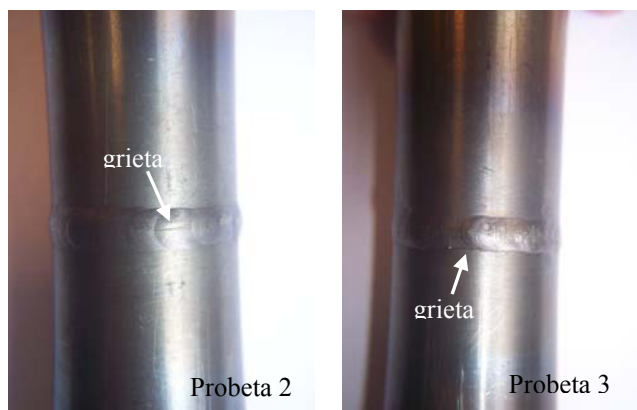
Aspecto de las probetas 2 y 3 tras el ensayo. Se puede observar que la grieta en la probeta 2 recorre la zona fundida del cordón de soldadura, mientras que en la probeta 3, se localiza en la zona afectada por el calor inferior adyacente a la soldadura.
